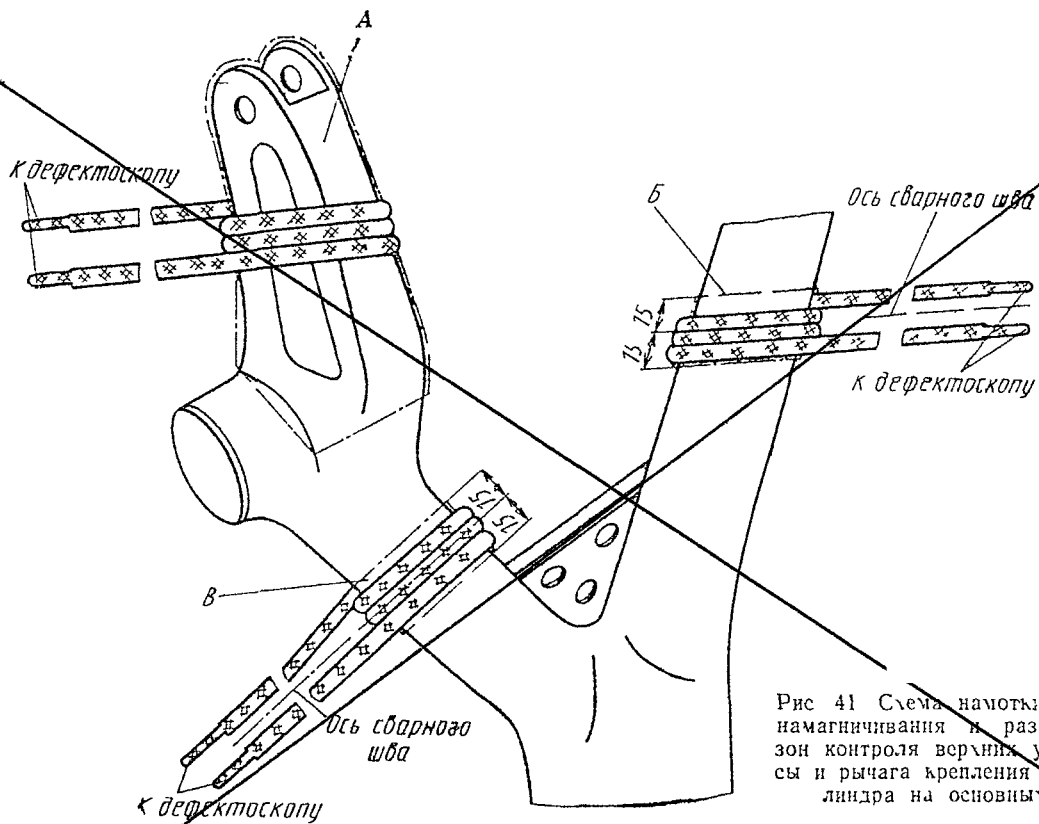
Схема намотки кабеля для намагничивания и размагничивания зон контроля верхних узлов траверсы и рычага крепления шлицового цилиндра на основных опорах
